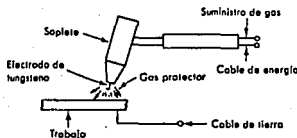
Esquema de soldadura al arco de tungsteno con gas con gas. El tungsteno no se funde para incorporarse al charco de soldadura. Este se conoce como electrodo no consumible.
